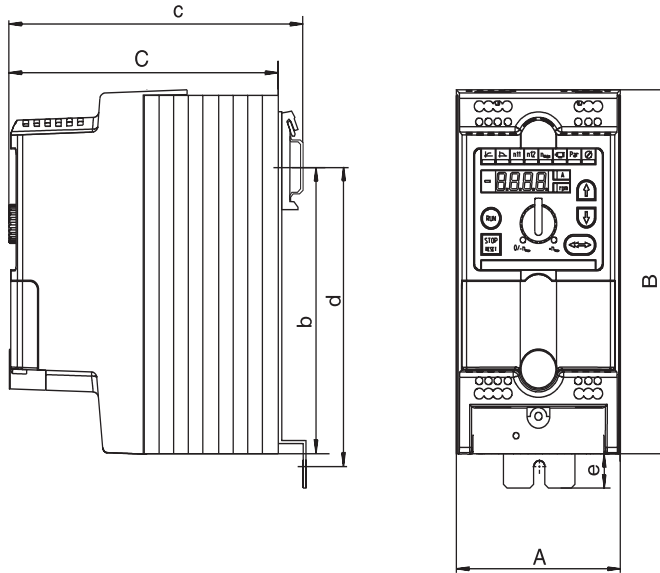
Габаритный чертеж MOVITRAC® 07 типоразмера 3
